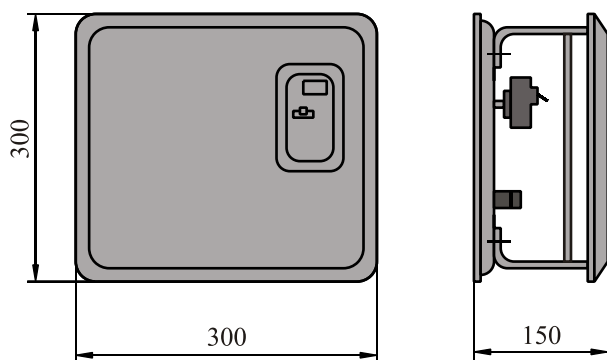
Внешний вид и габаритные размеры щитка ЩЭ1409
